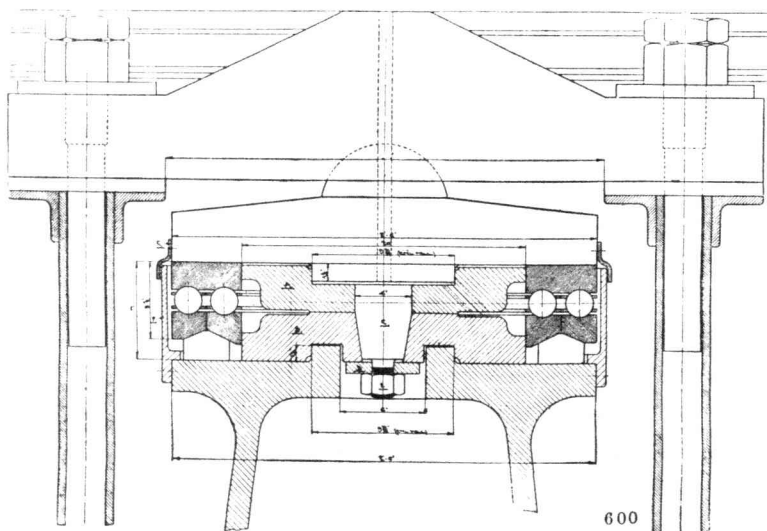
Drehscheibenzapfen mit schwedischem Kugellager für die australischen Staatsbahnen.
